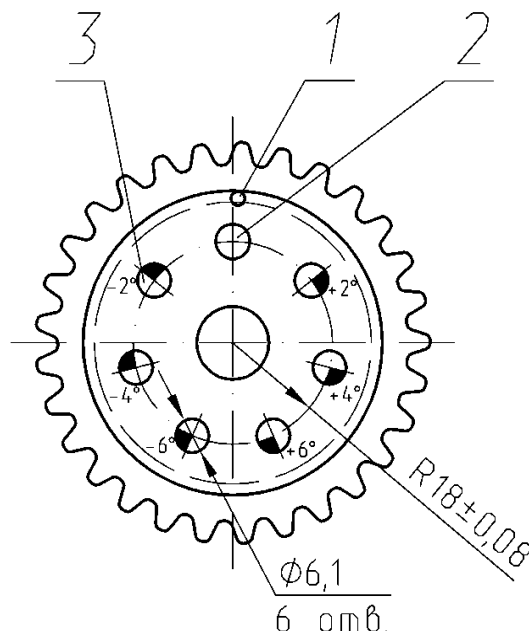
Звездочка распределительного вала с дополнительными отверстиями:
